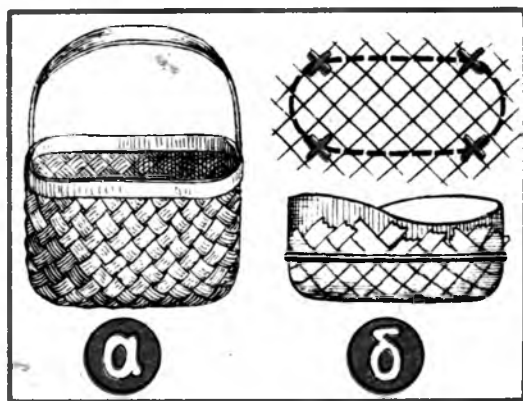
Получение овальной корзины из коробчатого полотна: а — корзина; б — полотно с разметкой мест поворота лент и контурами дна болванки и плетение полотна на болванке под резинкой
